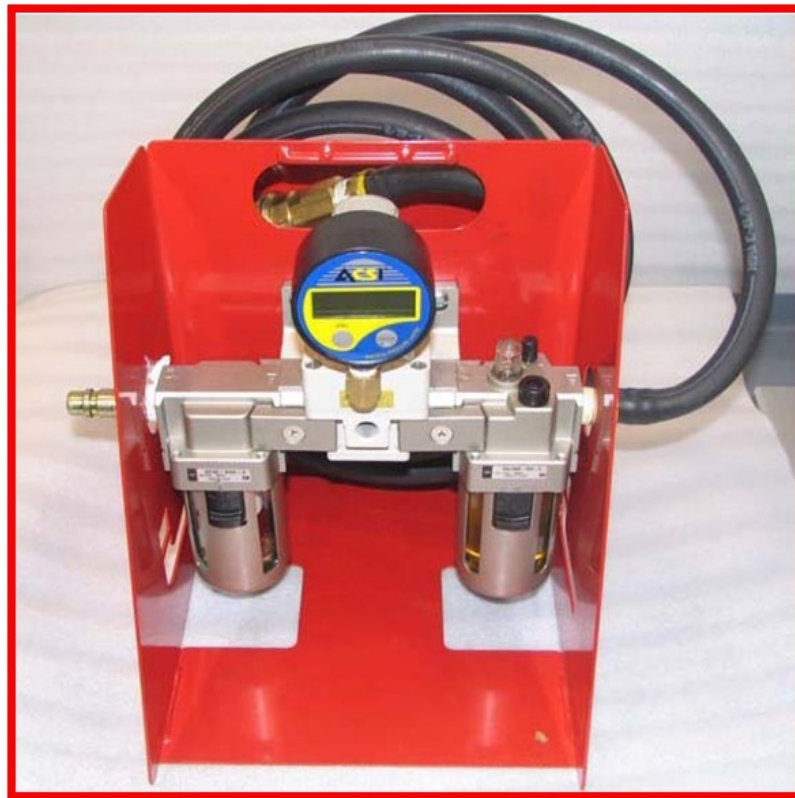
Блок подготовки воздуха для пневматической болтинг-машины JGUN.
